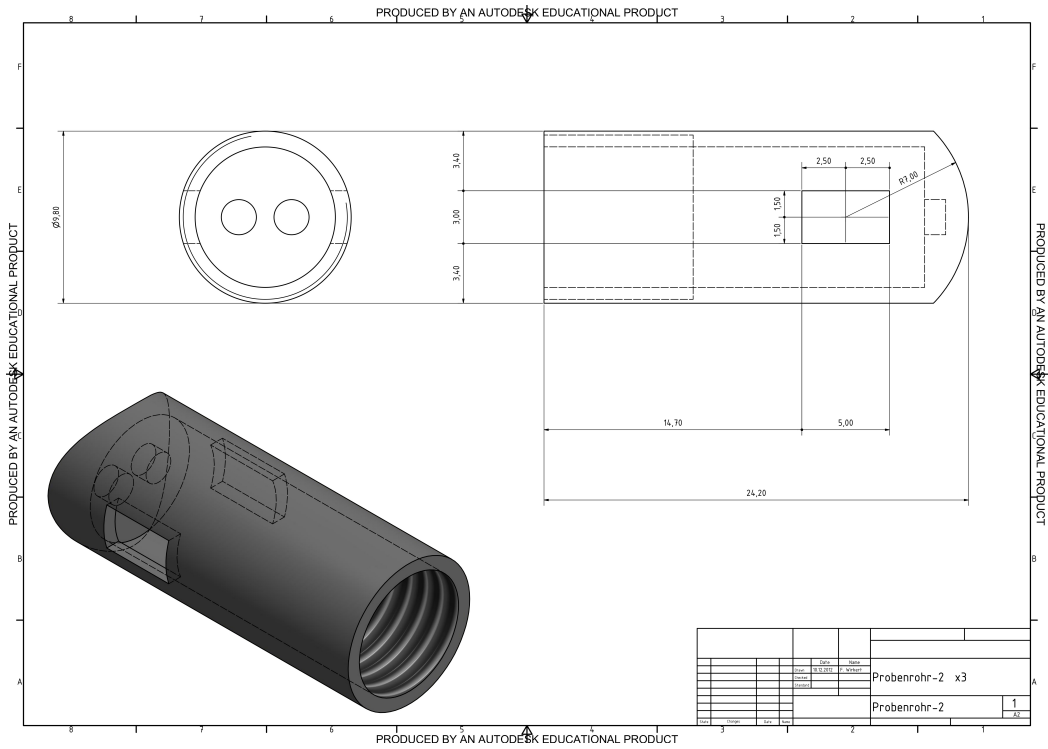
Technische Zeichnung Probenzelle 2
